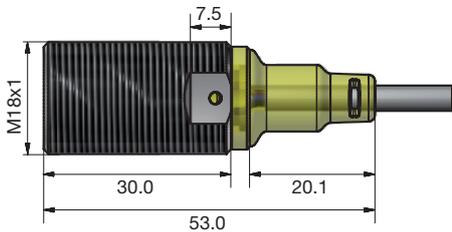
Lange Ausführung, bündiger Einbau, Steckversion
